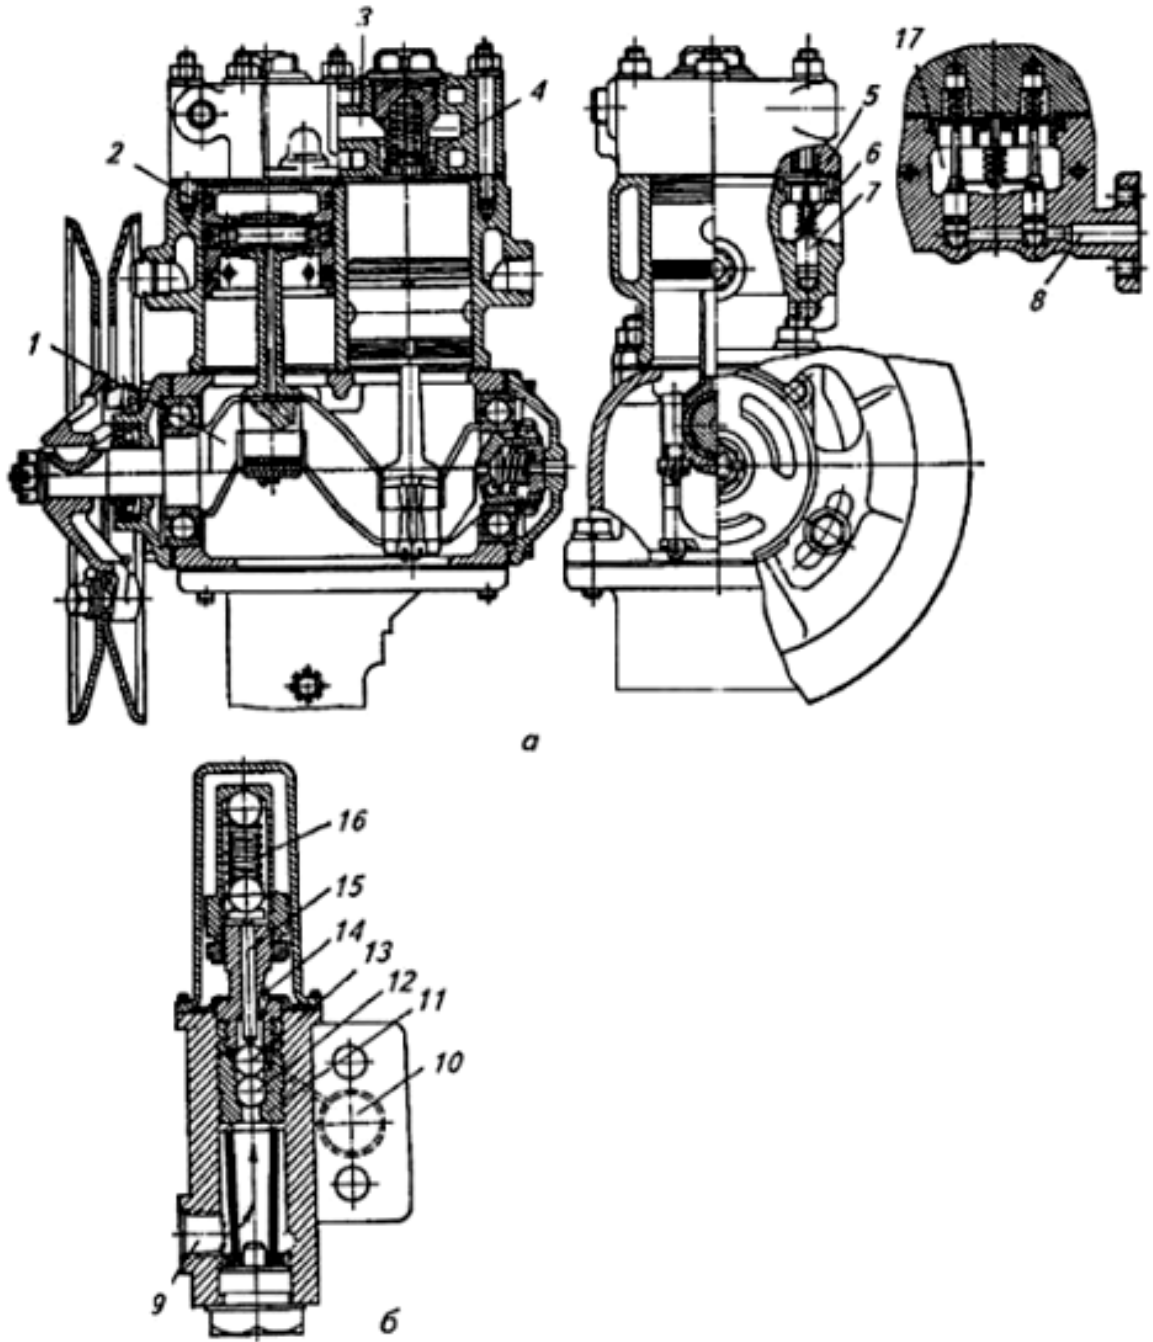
Компрессор и регулятор давления: а - компрессор с разгрузочным устройством; б - регулятор давления; 1 - коленчатый вал; 2 - поршень компрессора; 3 - воздушная полость; 4 - пластинчатый нагнетательный клапан; 5 - впускной клапан; 6 - пружина; 7 - плунжер; 8 - канал; 9, 10 - отверстия регулятора; 11 - втулка; 12, 13 - клапаны; 14 - боковой канал; 15 - шток; 16 - пружина регулятора; 17 - воздушная камера
